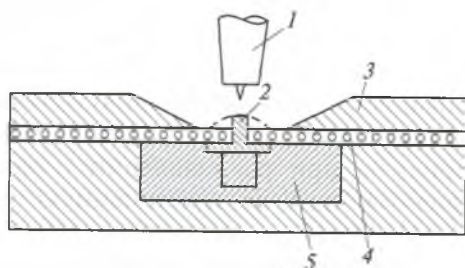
Схема сварки листового КМ ВКА-2 через промежуточную расплавляемую Т-образную вставку:
